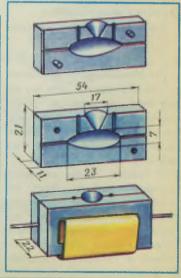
Штамп для получения заготовки лепестка: а — пуансон; б — матрица; в — приспособление в работе.
